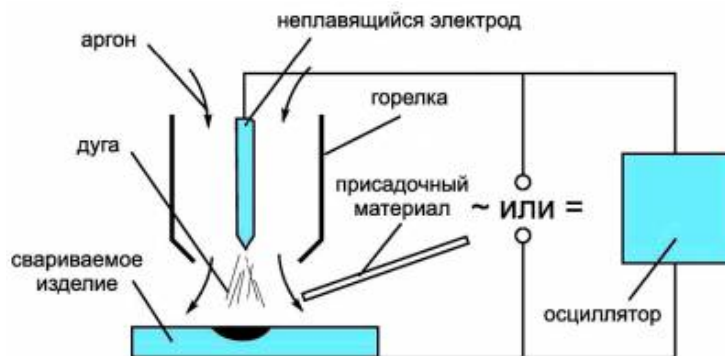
Схема процесса сварки в защитных газах неплавящимся электродом
